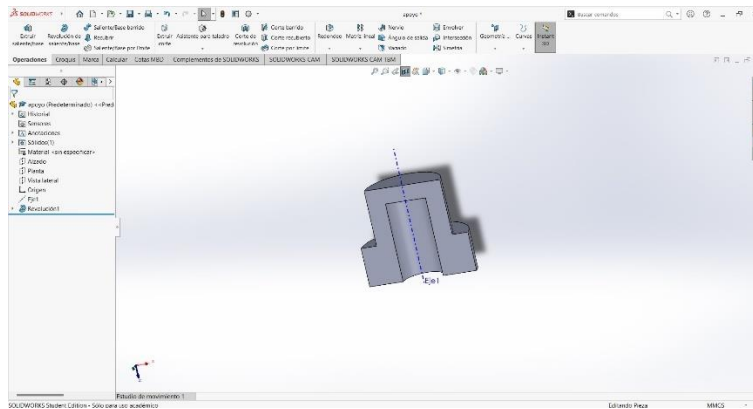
Corte de pieza Taqué. Fuente: SolidWorks
